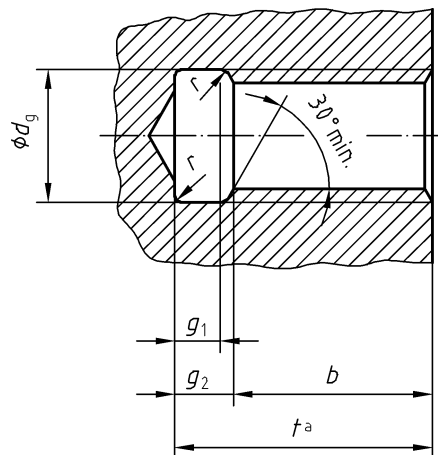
Gewindegrundloch mit Gewindeauslauf
